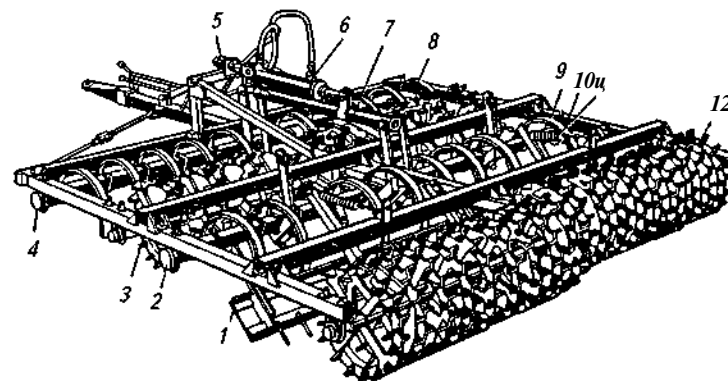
Комбинированный почвообрабатывающий полунавесной агрегат РВК-3,6:
